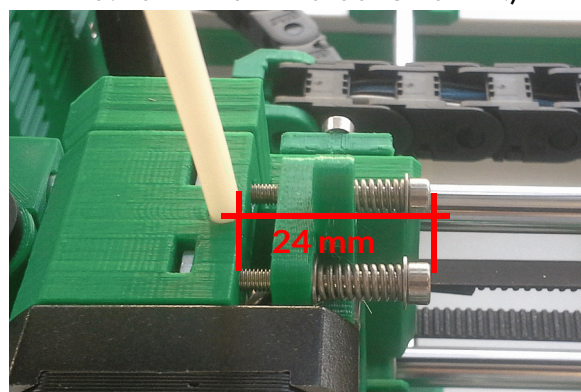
Einschraubtiefe der Andruckschrauben
